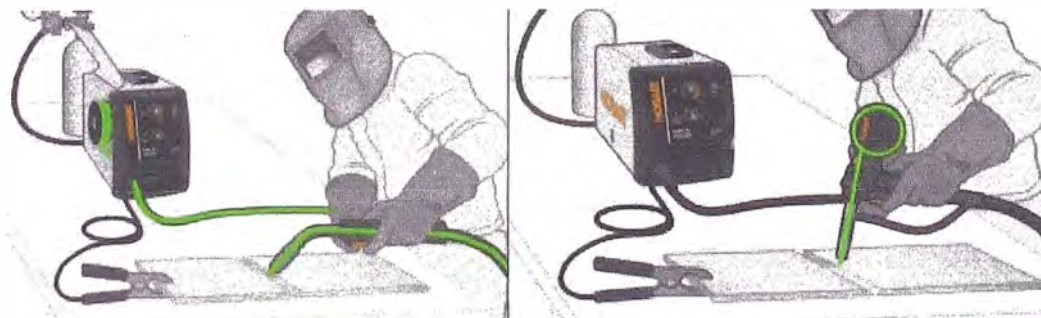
Disposición para soldadura de arco metálico protegido por gas (Fuente: Hobart Welders)
